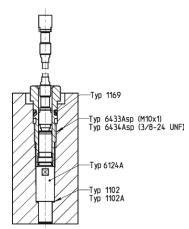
Einbau des Sensors Typ 6124A... mit Montagehülse
